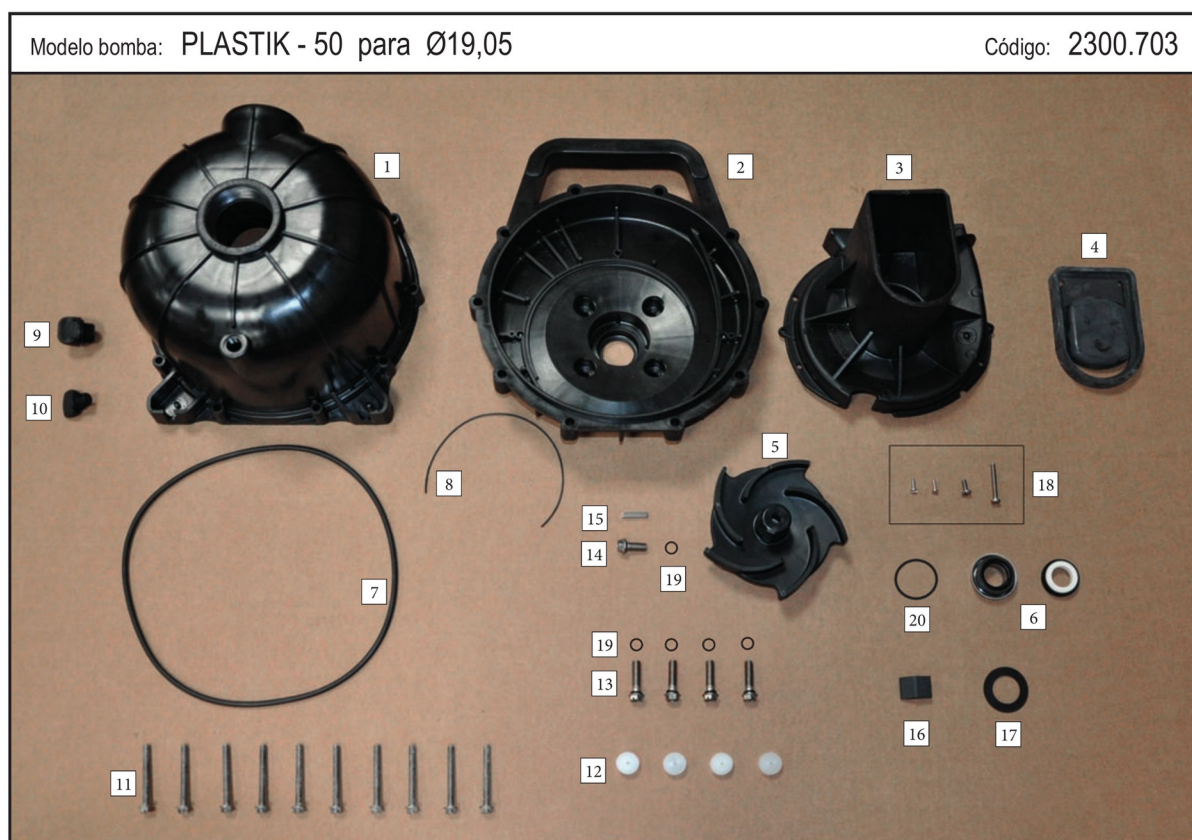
Despiece de la bomba PLASTIK 50 (cód. 2300.703)
